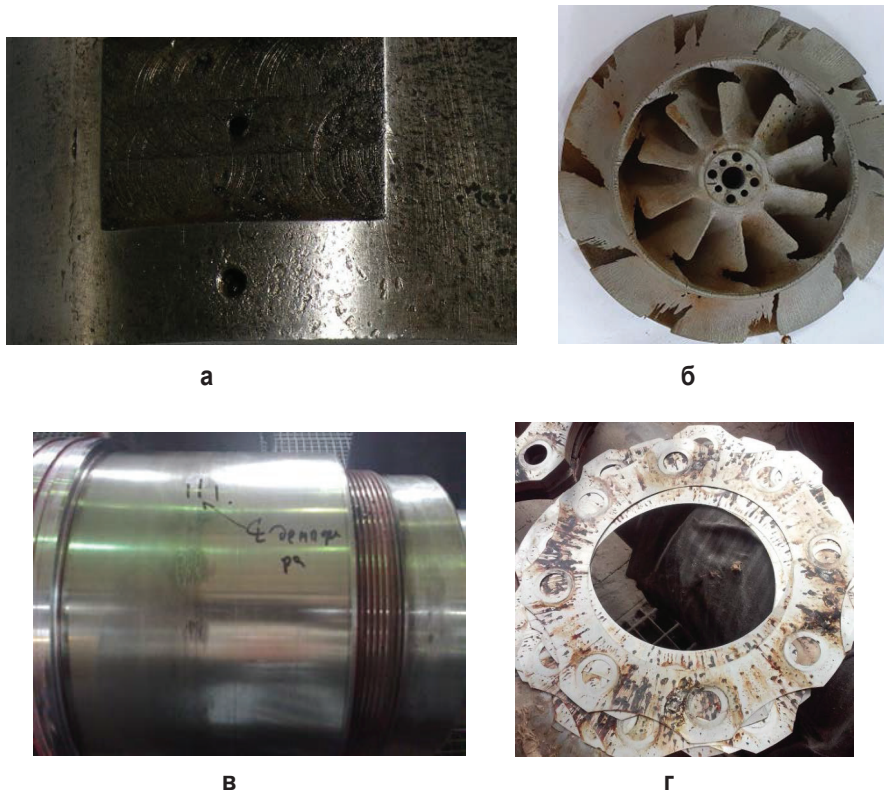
Поверхня вкладишу підшипника, пошкоджена щілинною корозією (а), хімічна корозія робочого колеса (б), фреттинг корозія шийки валу відцентрового насосу (в) і поверхонь гнучких елементів пружної муфти (г)
